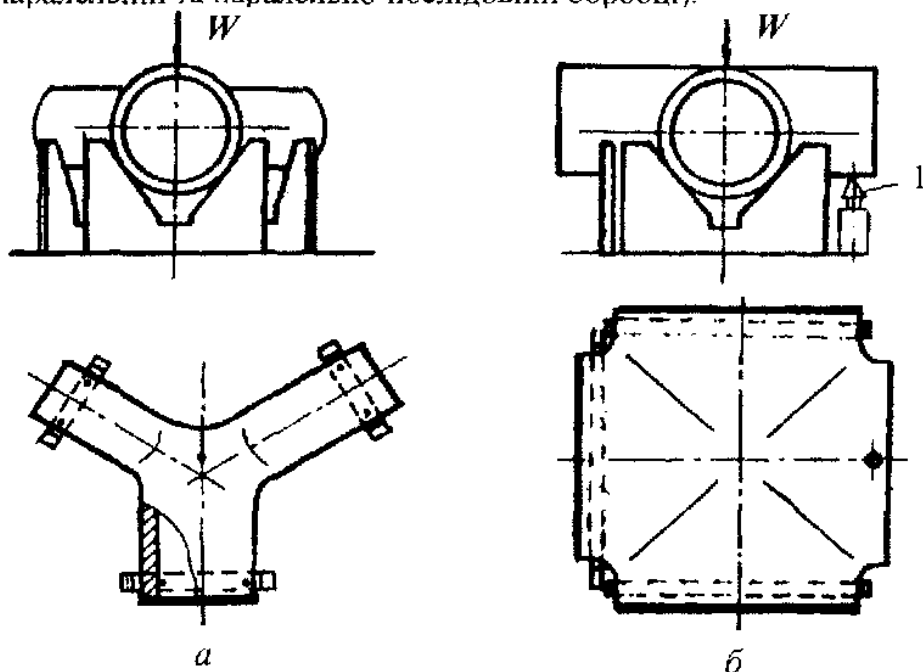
Схеми встановлення заготовок на зовнішні циліндричні поверхні з перехрещеними осями
